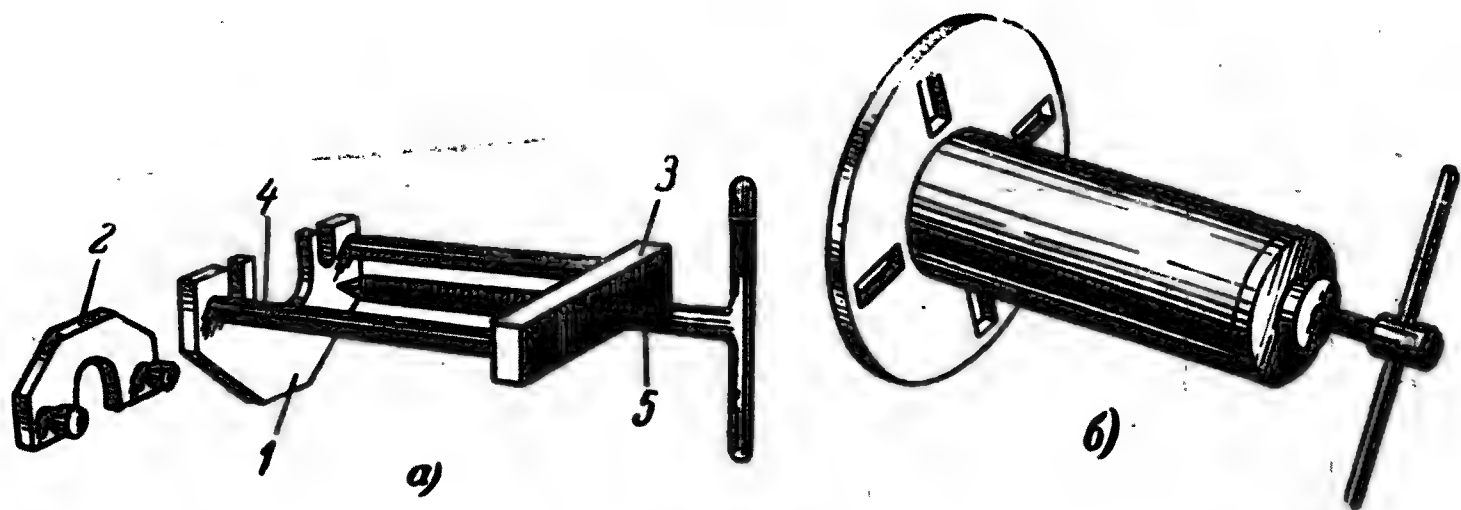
Съемник для шариковых и роликовых подшипников.
